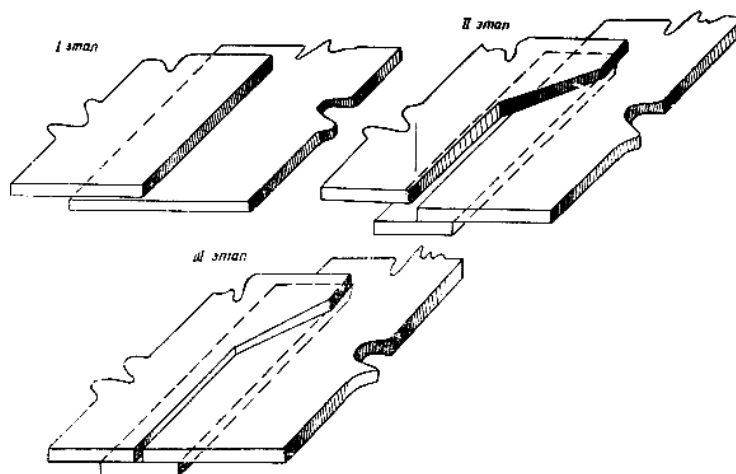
Этапы сборки окраек на подкладке при изготовлении днища вертикального резервуара
